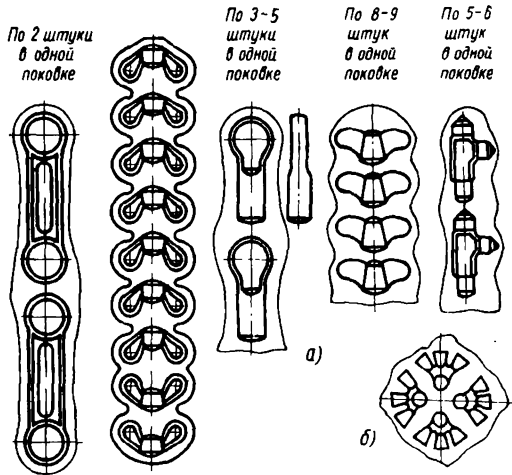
Поковки, получаемые парной или многоштучной штамповкой: а — поковки гр. I; б — поковки гр. II
